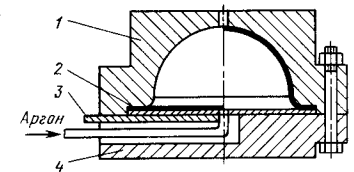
Схема штампа для формовки полушера из титановых сплавов в состоянии сверхпластичности:
